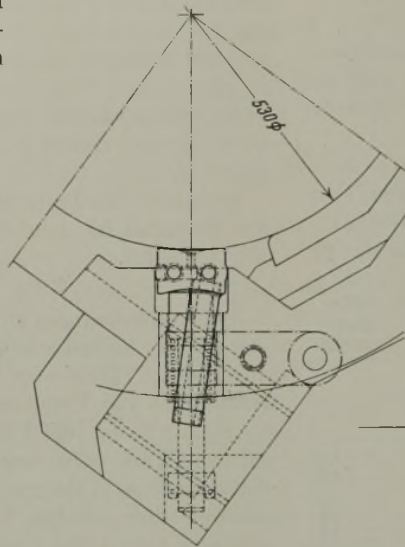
Fettzuführung zum Einbaustück und Zapfen.
